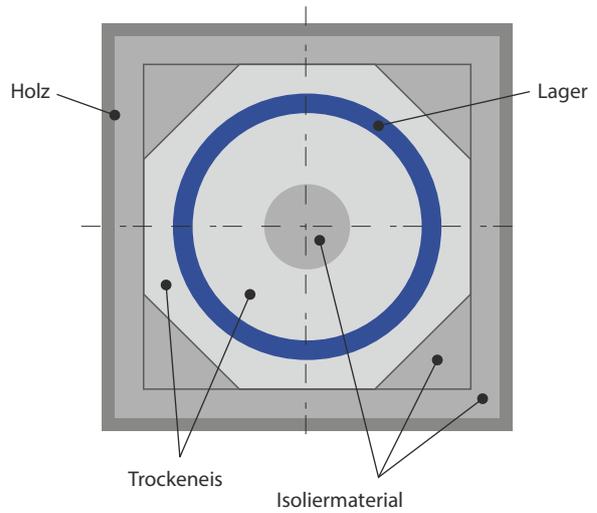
Holzbehälter für Trockeneis (Aufsicht)
